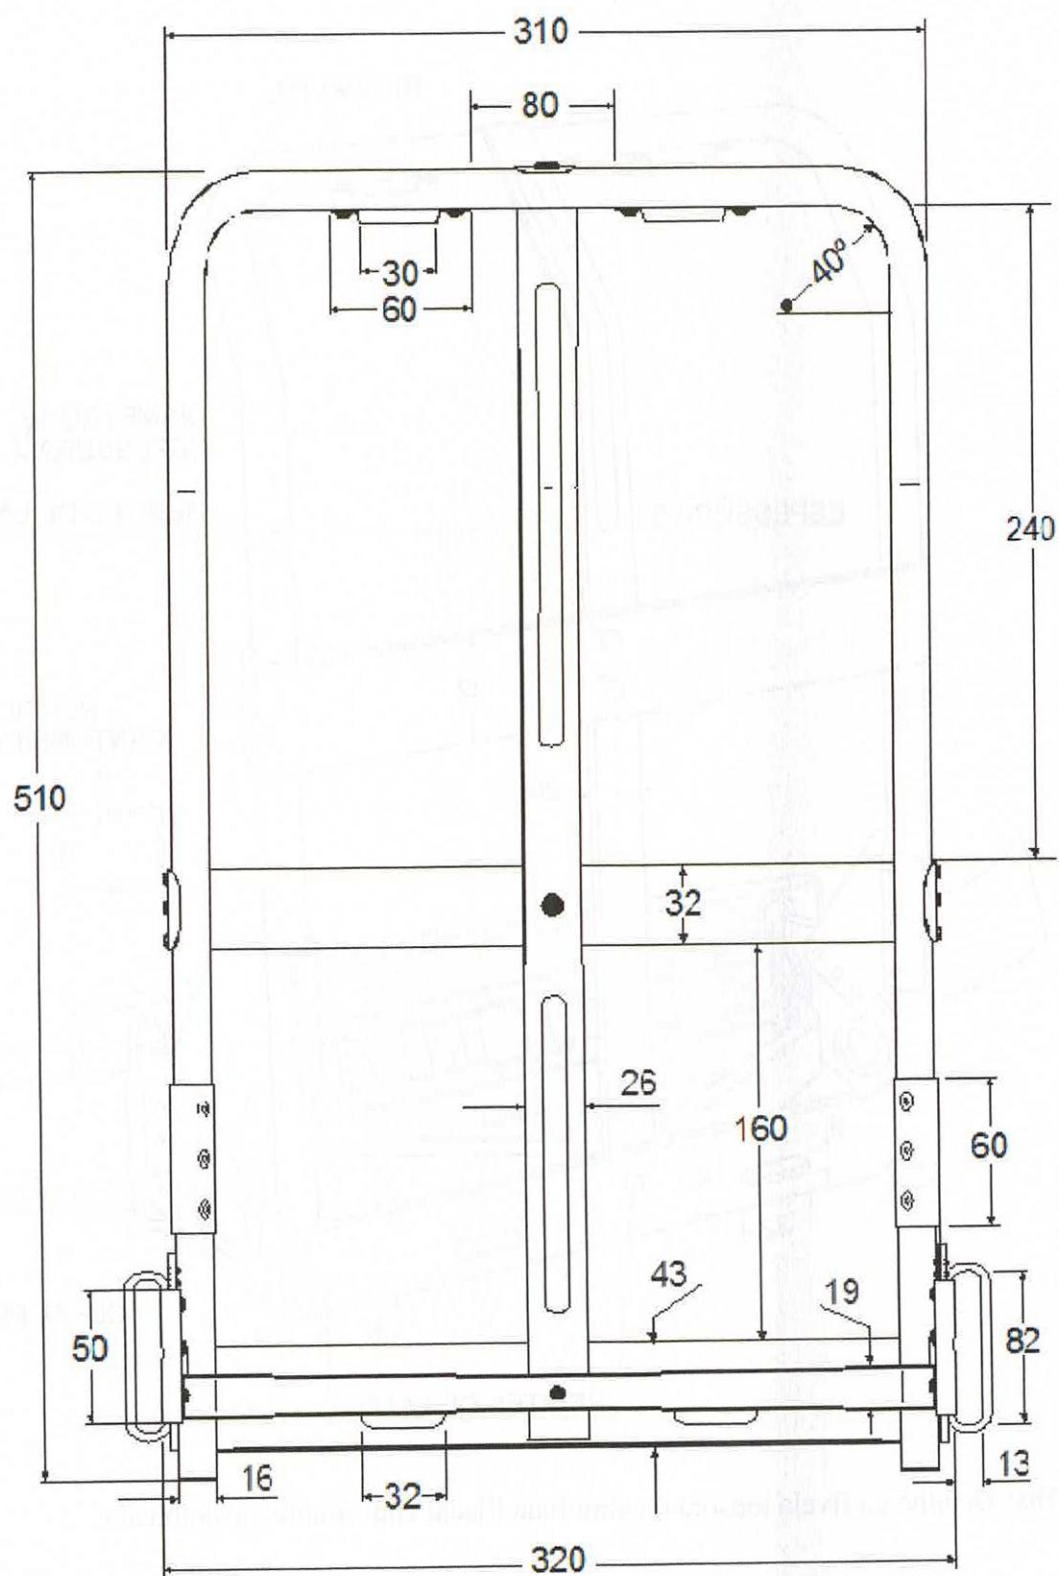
Vista frontal do suporte metálico (medidas em mm)
